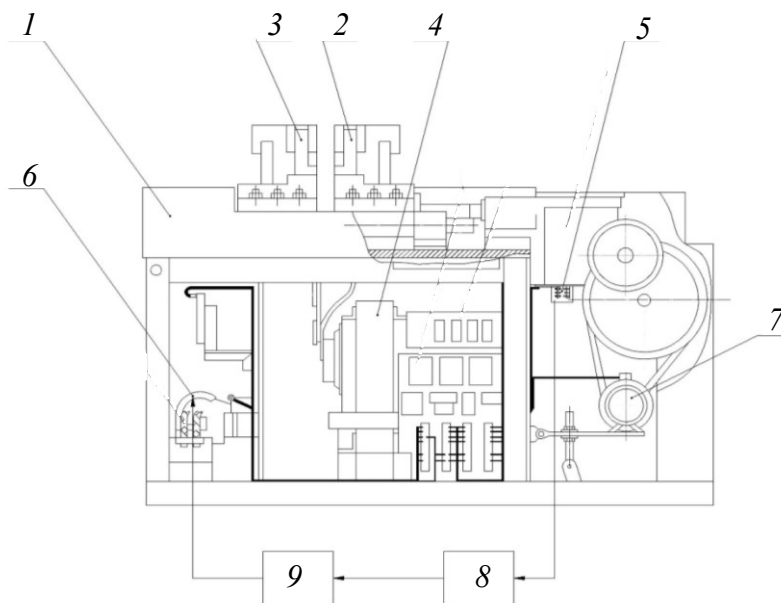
Общий вид машины для контактной стыковой сварки МС-2008М:
